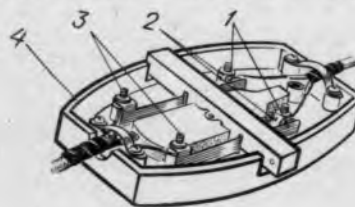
Устройство проходного выключателя: 1— подвижные контакты, 2— неподвижные контакты, 3— зажимные винты, 4— корпус.
